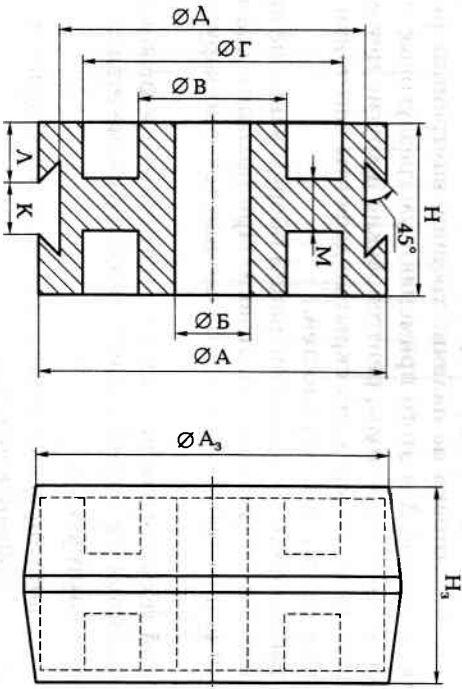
Эскиз обрабатываемой дискообразной детали:
